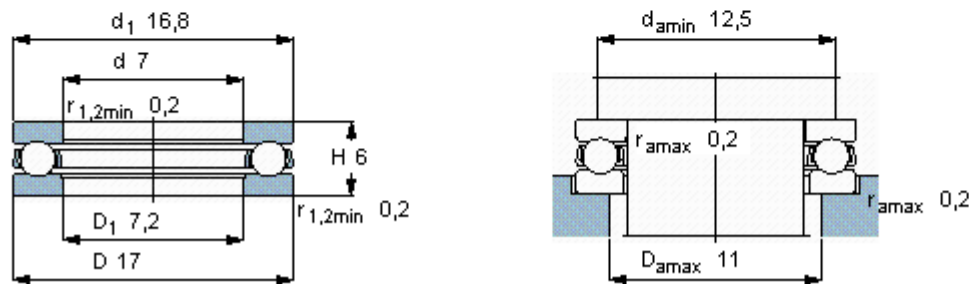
Características del rodamiento SKF-BA-7. Fuente: [www.skf.com](http://www.skf.com)
